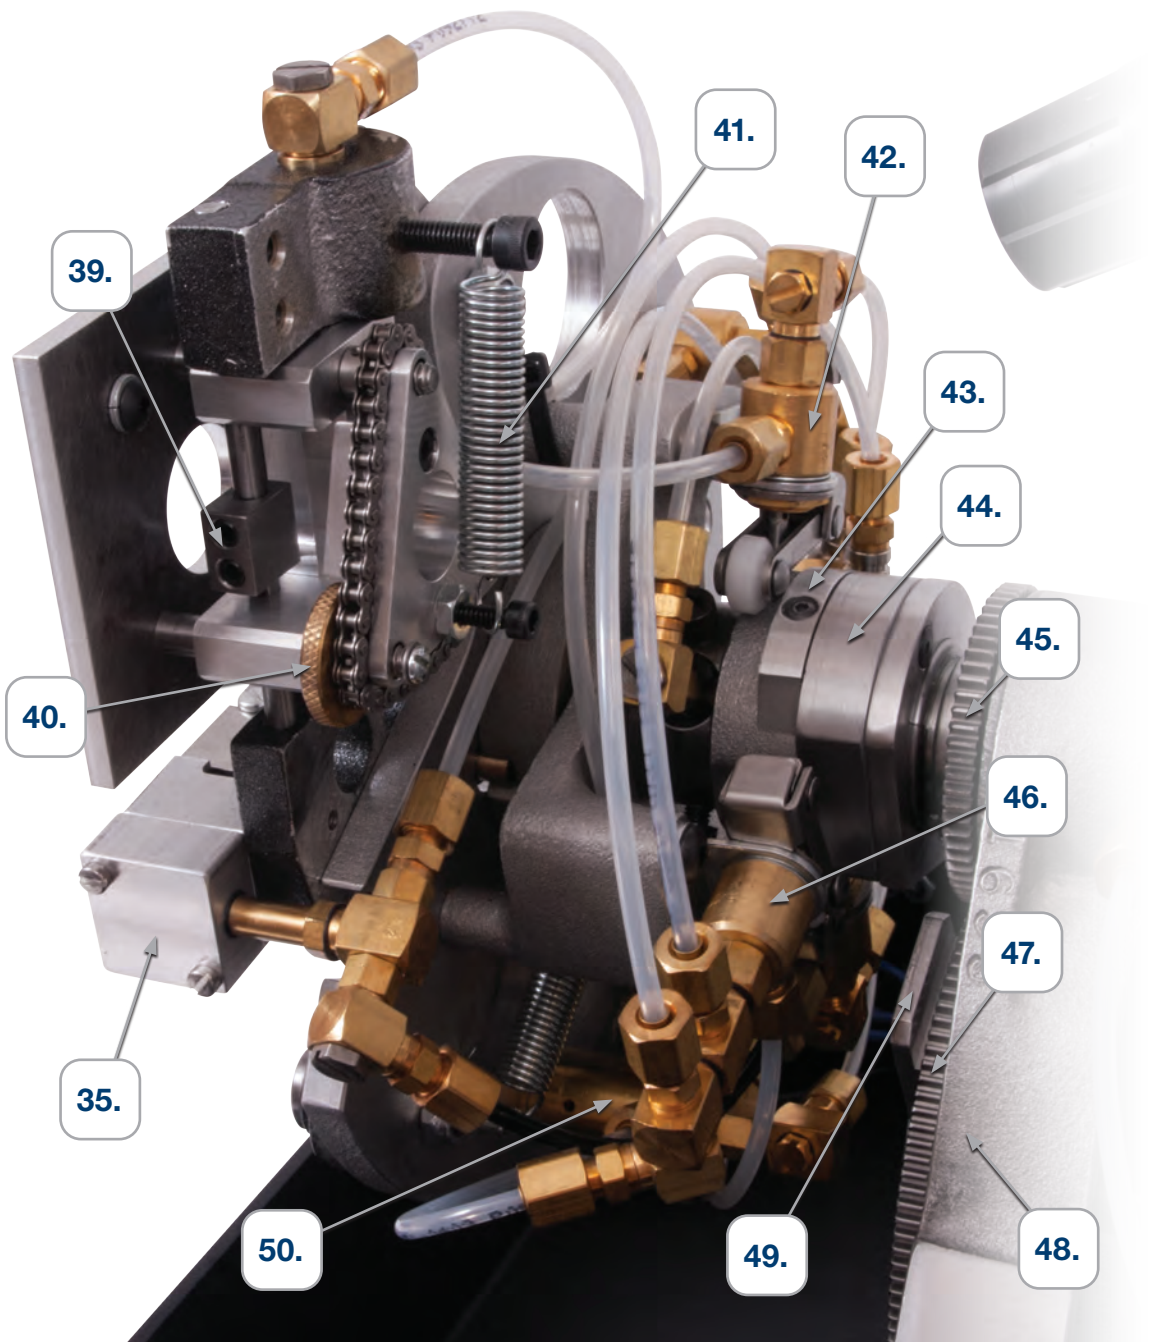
ENSEMBLE DU GRAND BRAS DE SERRAGE – VUE AVANT
